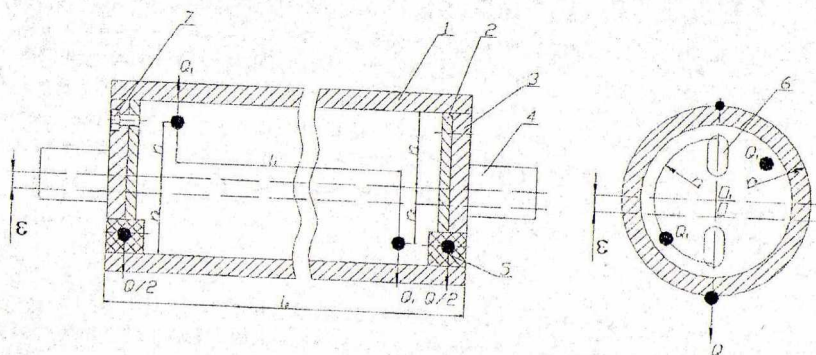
Конструкція вала гвинтового очисника зі зміщеною віссю обертання: 1-труба; 2-диск; 3-фланець; 4-опора; 5-противаги; 6-пази; 7-кріпильні елементи
